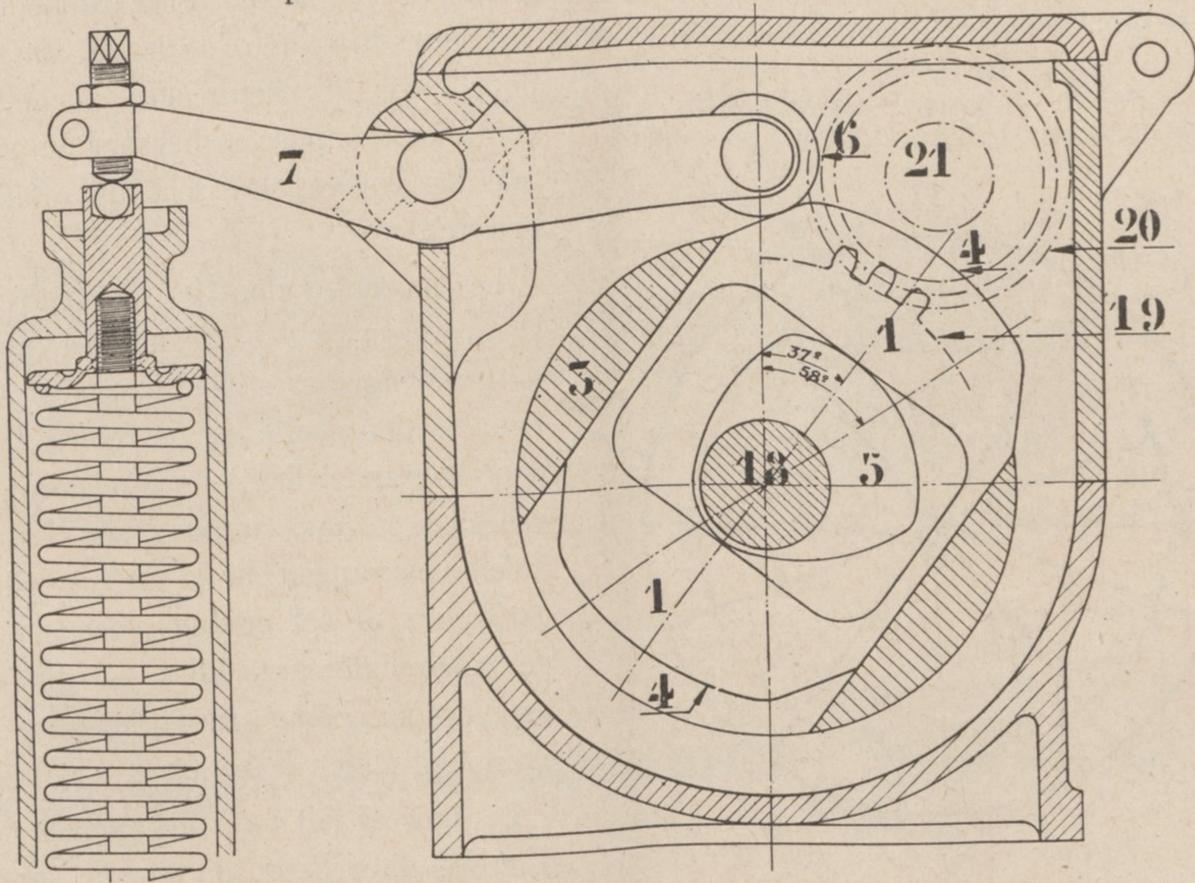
MÉCANISME DE DISTRIBUTION. (Côté gauche de la machine vue de l'arrière).
